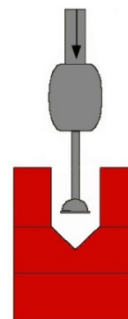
Das Werkzeug seitwärts in Richtung Bohrungswand bewegen bis sich die Achse des Werkzeughalters im Durchmesser der auszuführenden Kreisbewegung befindet.
